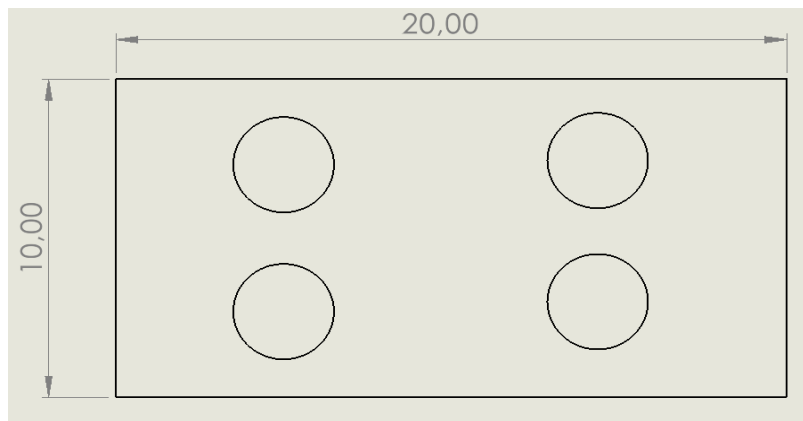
Cotas das chapas de ângulo reto em milímetros. (Autor,2021)
